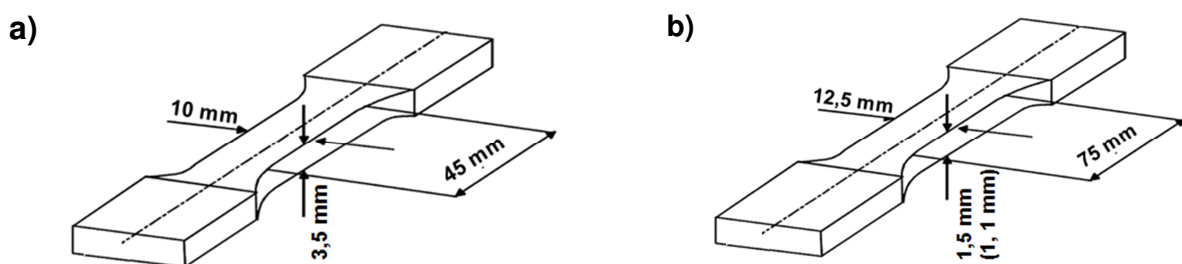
Zugprobengeometrie : a) Form E DIN 50125 b) Form H DIN 50125
